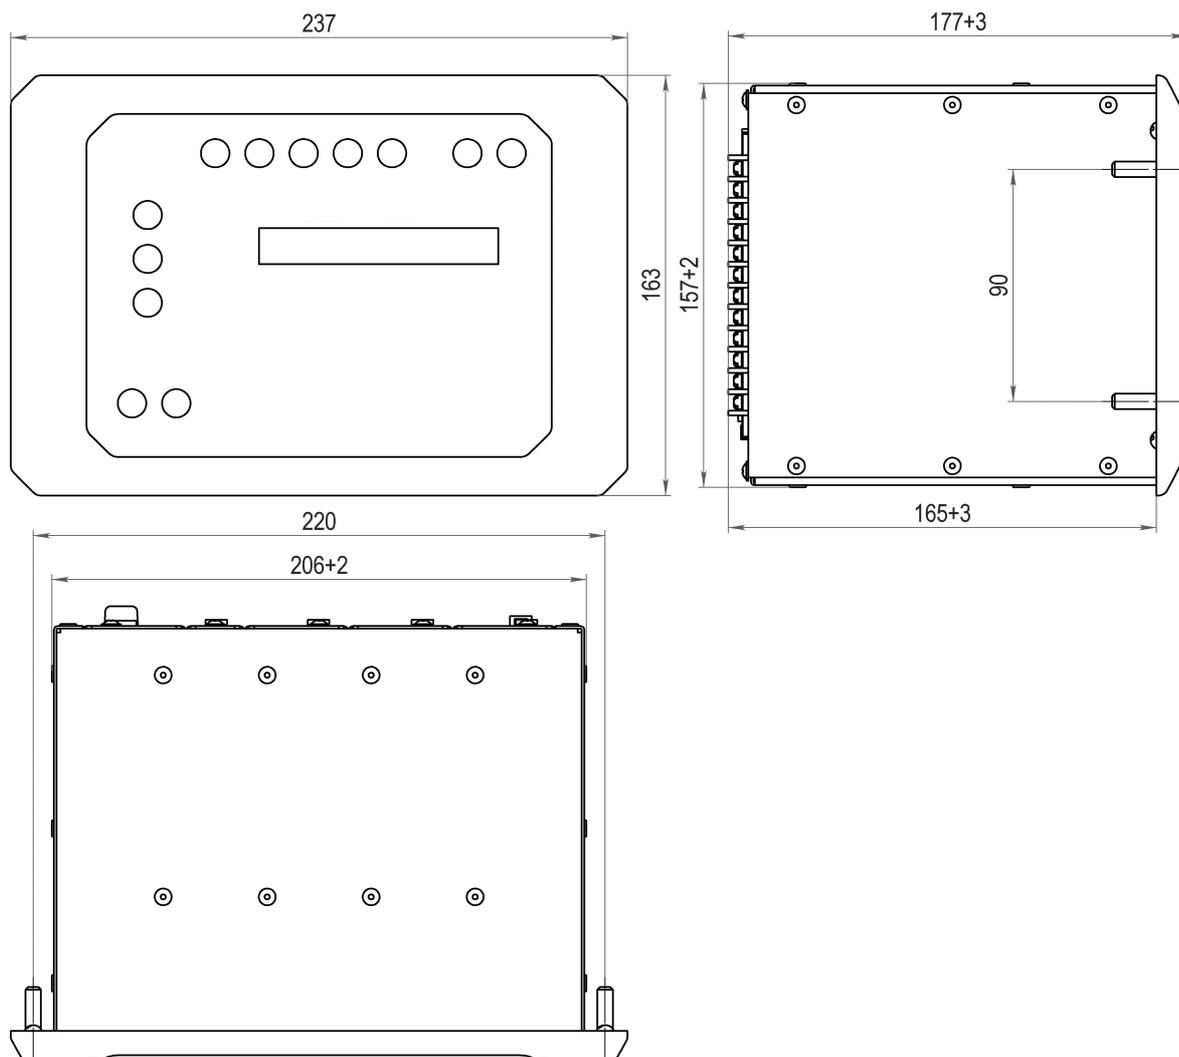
Габаритные размеры устройства УМПЗ/ТЭК.
